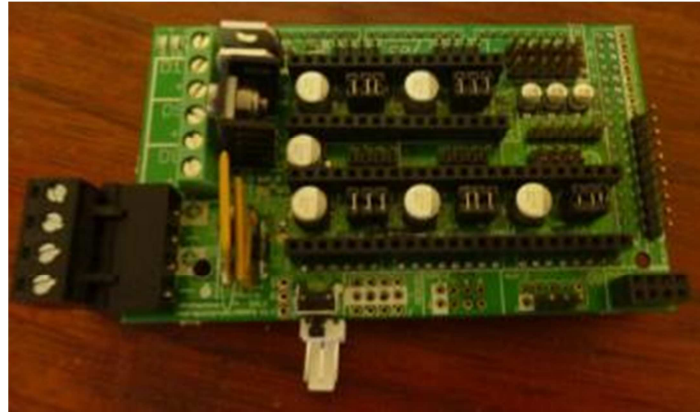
Conector para Reset instalado en la RAMPS 1.4
